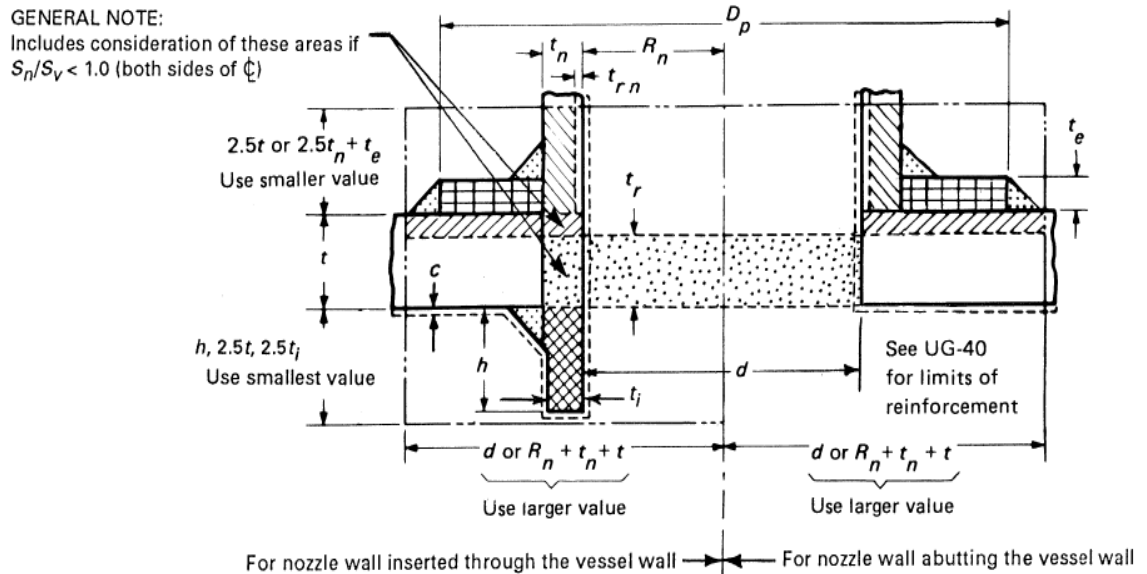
denominación de áreas de soldadura. Fuente: [37].
